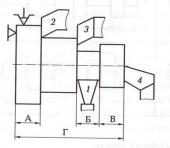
Схема обработки на токарно-револьверном станке:  $1\!-\!4$  — резцы
